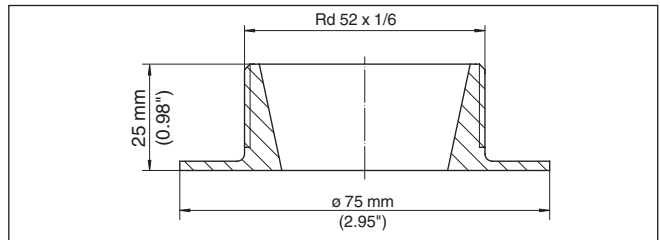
Maße Einschweißstutzen Konusanschluss DN 25
